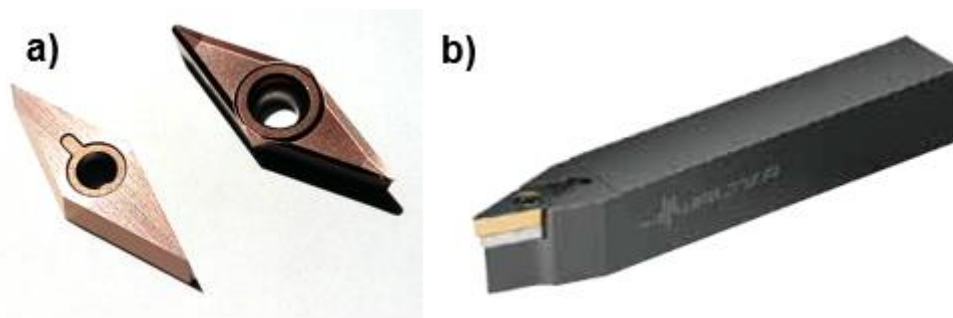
Ferramentas: a) Inserto de metal duro; b) Porta-ferramenta.
